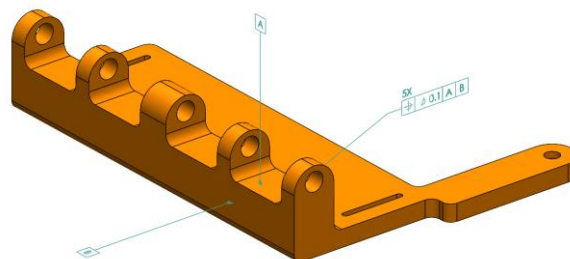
Tolerancias geométricas “Apoyo mano”
